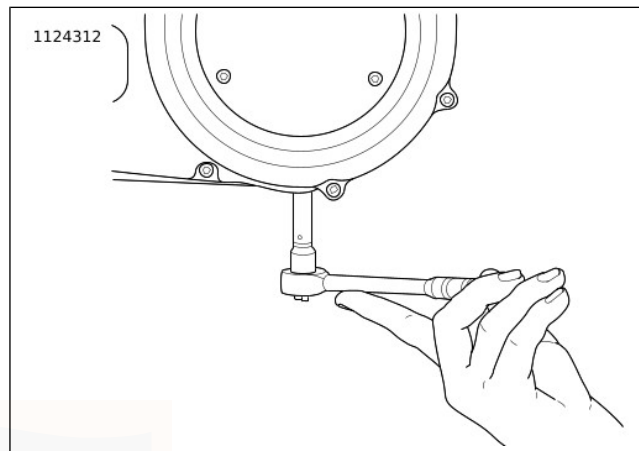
Ausbau/Einbau der Kettengehäuse-Ablassschraube
